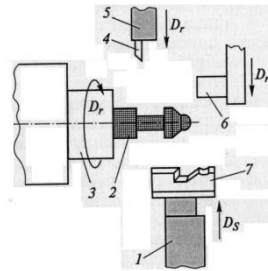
Схема обробки заготовки на фасонно-відрізному автоматі
